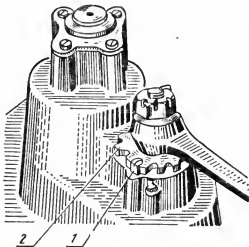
Регулировка бокового зазора между зубьями цилиндрической пары шестерен рулевого управления трактора ДТ-24:
